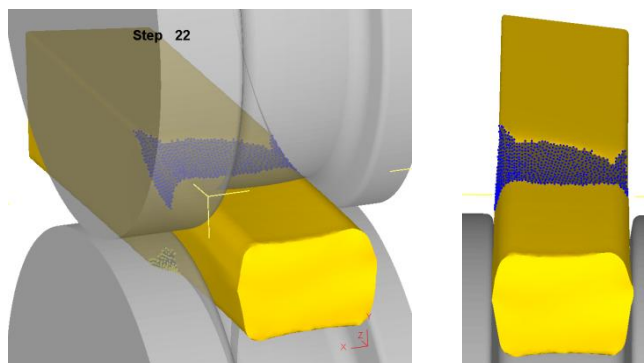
Точки контакта заготовки с поверхностью валка на стадии установившегося процесса прокатки заготовки с величиной ромбичности 20 мм и начальным углом поворота заготовки  $6^\circ$
